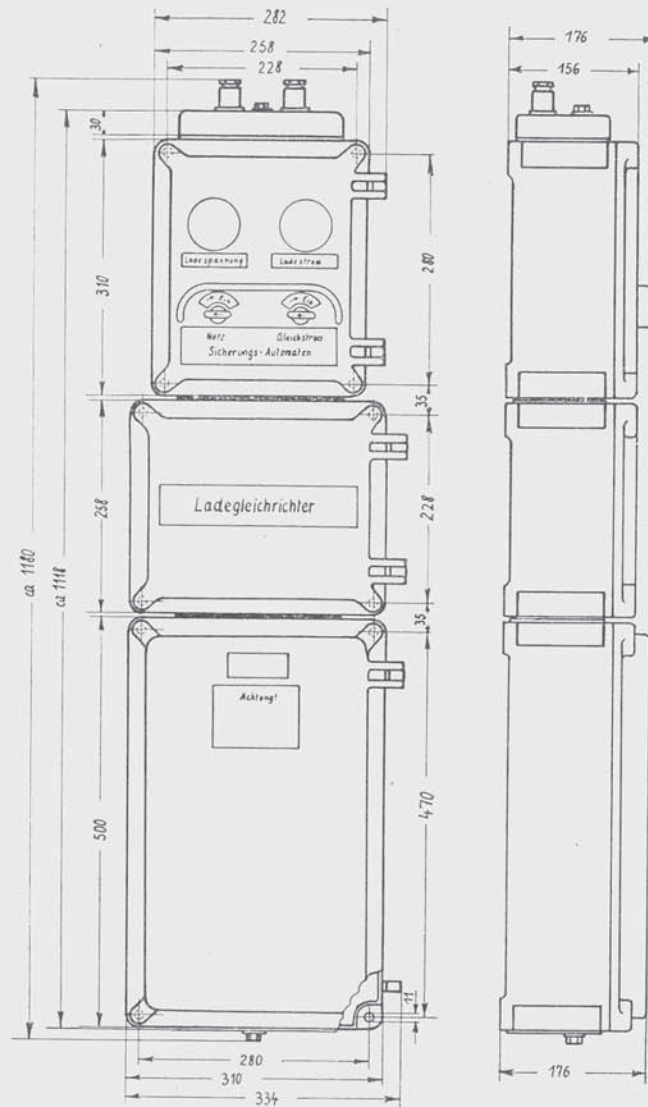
Ladegleichrichter für 15 A, Maßbild
